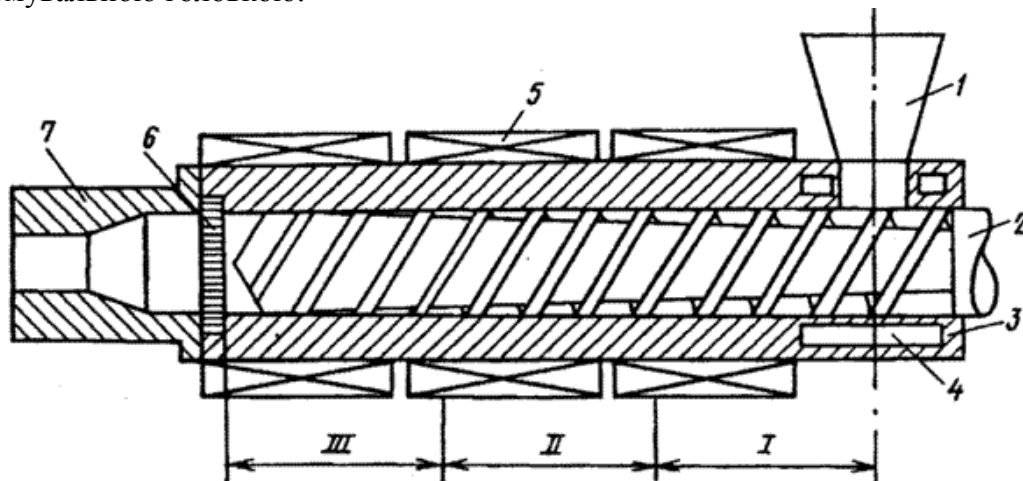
Схема одношнекового екструдера: 1 – бункер; 2 – шнек; 3 – циліндр; 4 – порожнина для циркуляції води; 5 – нагрівник; 6 – решітка із сітками; 7 – формувальна головка
